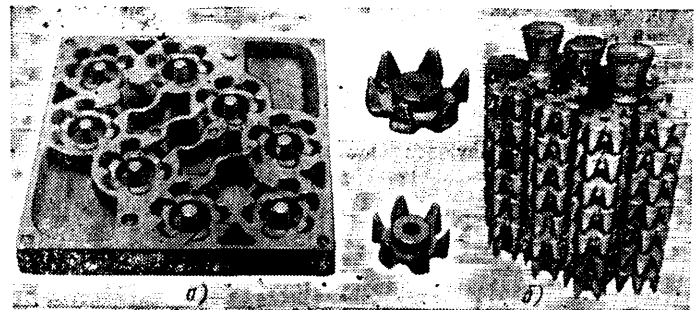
Полуформа и отливка детали генератора (а) и блок отливок (б)
